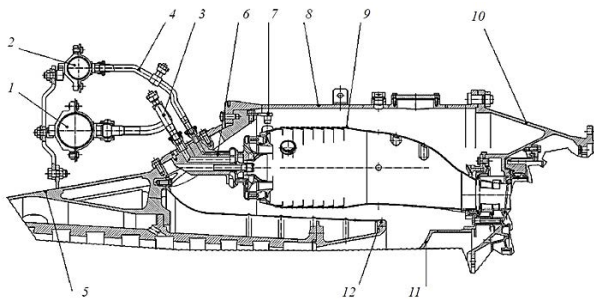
Камера згоряння ГТД потужністю 25 МВт: 1, 2 – паливні колектори; 3, 4 – підведення паливної суміші; 5 – корпус компресора високого тиску; 6 – пальник; 7 – фіксатор; 8 – корпус камери згоряння; 9 – жарова труба; 10 – силовий корпус; 11 – дифузор; 12 – внутрішній корпус
